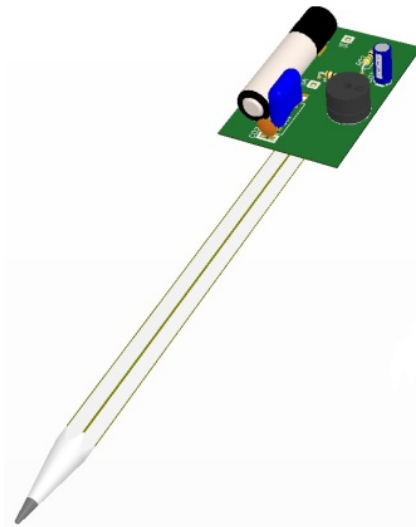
Croqui de montagem do dispositivo eletrônico DRAWDIO.
